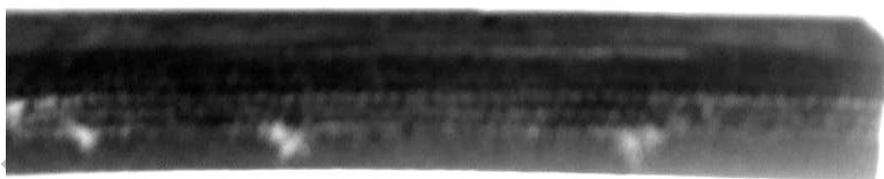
Качество реза резины при резке на фрезерно-отрезном станке
